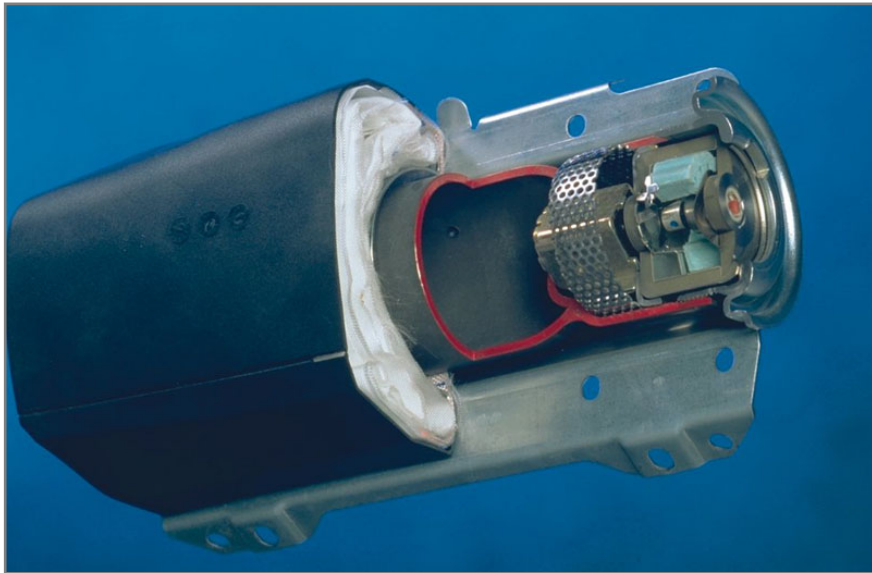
VUE EN COUPE D'UN MODULE AIRBAG PASSAGER AVEC GÉNÉRATEUR DE GAZ HYBRIDE - AUTOLIV
